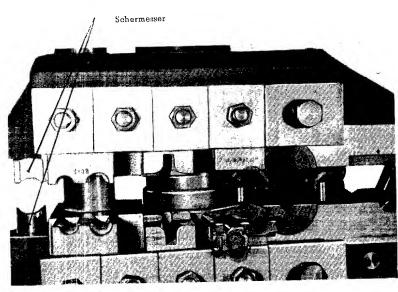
Vorderansicht des gehobenen Maschinenkopfes mit eingebauten Matrizen und Gesenke
